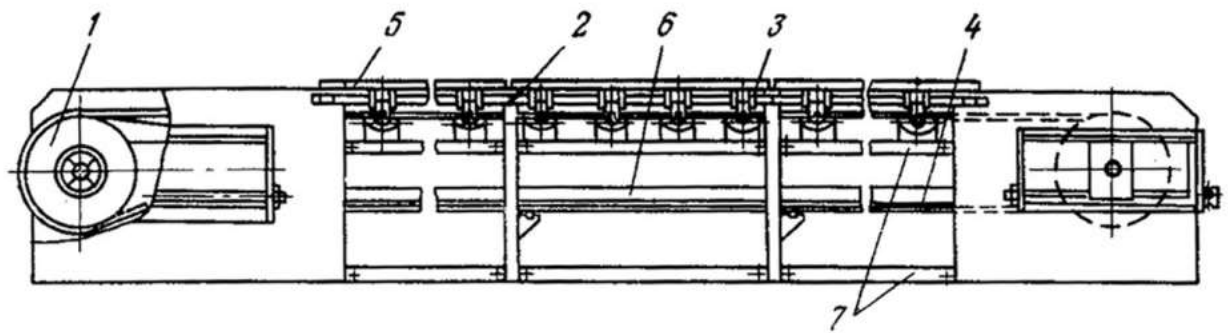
Принципова схема стрічкового конвеєра КЛЗД:
